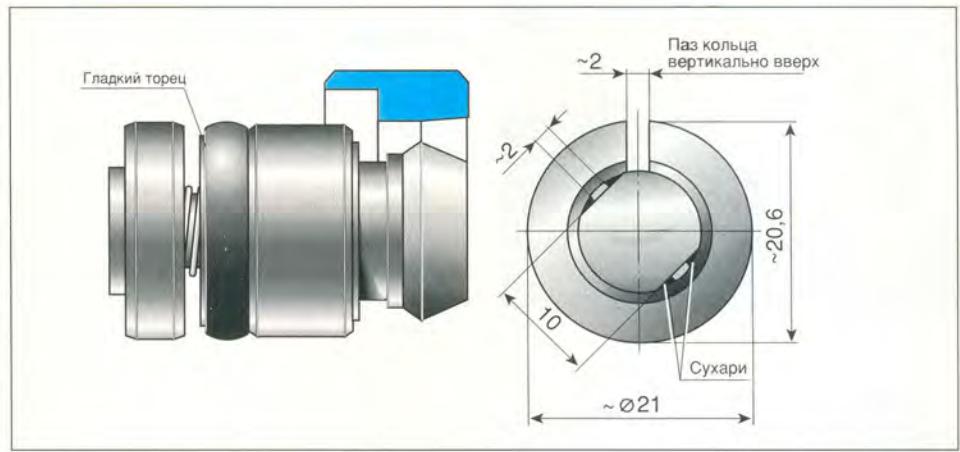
Так устанавливаются упорное кольцо и сухари.
